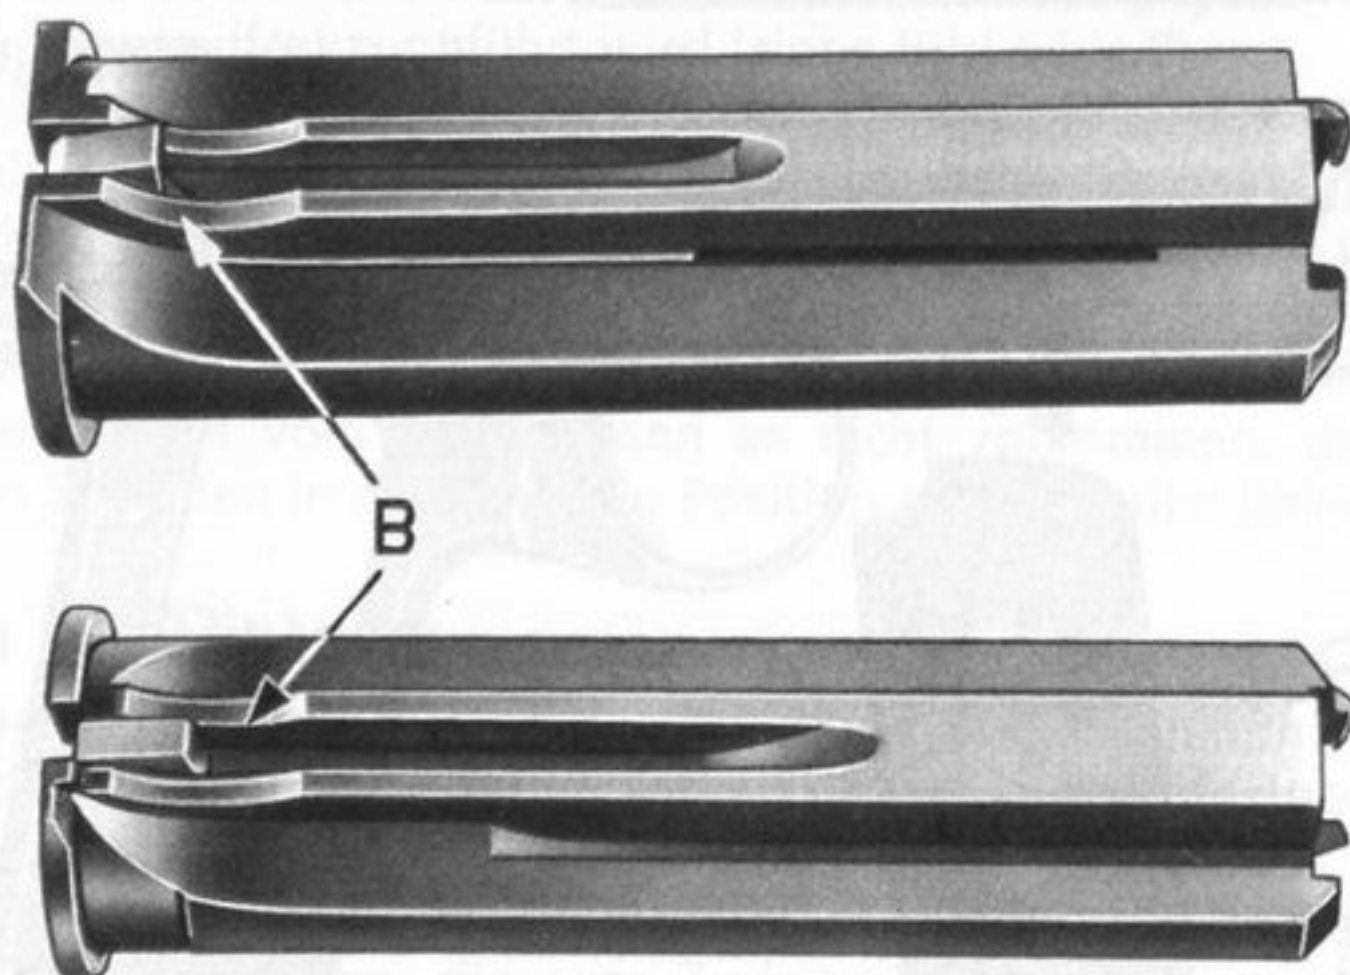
Verschußzylinder mit Schlagbolzen. Oben für Kaliber 7,65 mm, darunter für 6,35 mm. B = Ausnehmung für die Abzugstange
